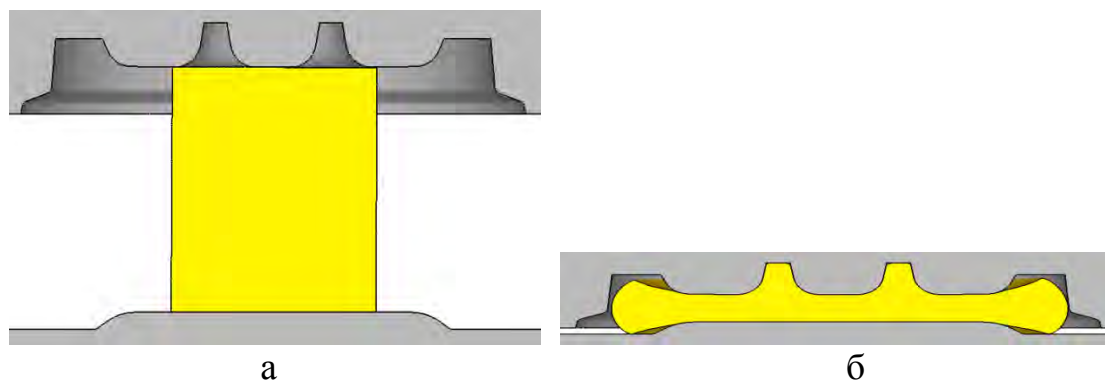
Формоизменение металла при черновой штамповке: а – начальный момент штамповки; б – конечный момент штамповки
